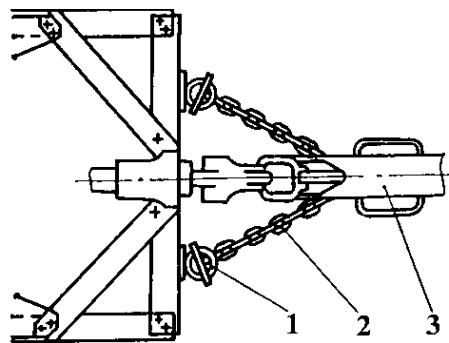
Схема крепления компрессорной станции предохранительными цепями
